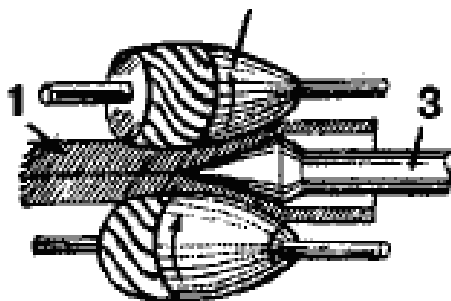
20. Схема валкового стану Меннесманів: 1– заготовка; 2– валки; 3 – стрижень [26].
